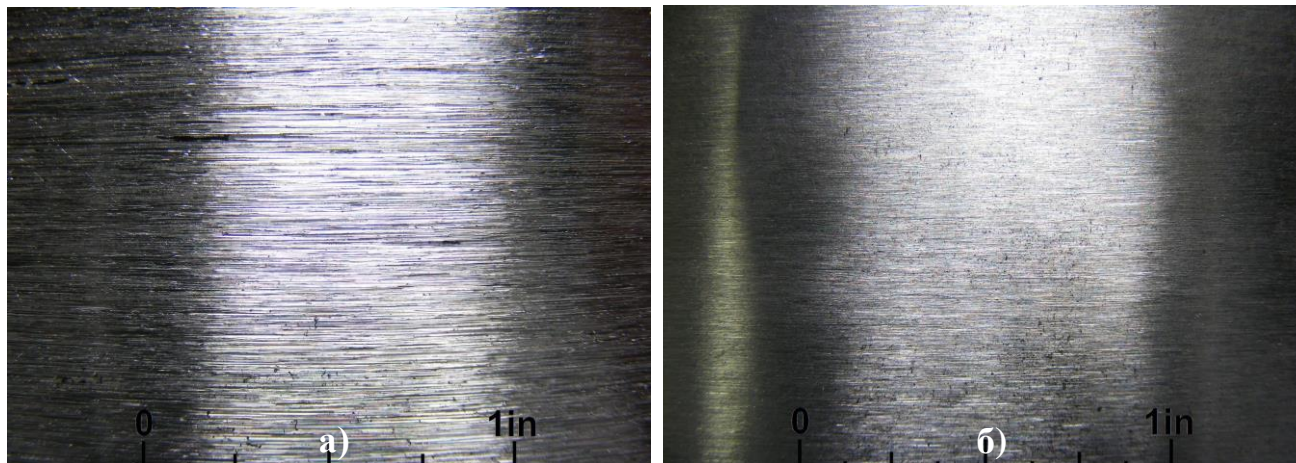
Внешний вид поверхностей стали после очистки мягким шлифовальным кругом: а – шероховатость 60 мкм при зернистости абразива P24; б – шероховатость 25 мкм при зернистости абразива P120 (б).
